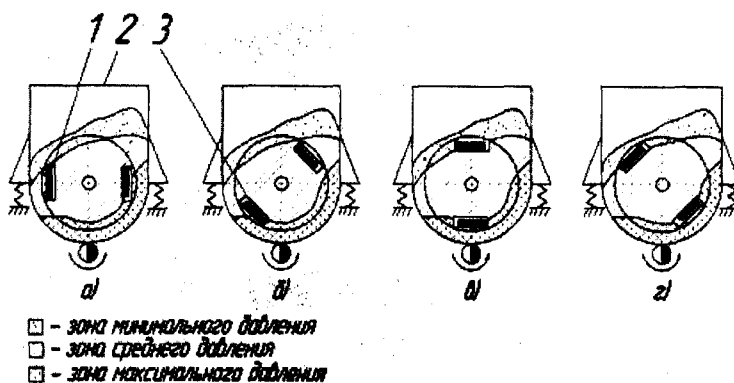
Схема прохождения деталей через зоны давления рабочей среды при вращении приспособления: 1 – обрабатываемый фрагмент; 2 – рабочая камера; 3 – решетчатый отсек приспособления
